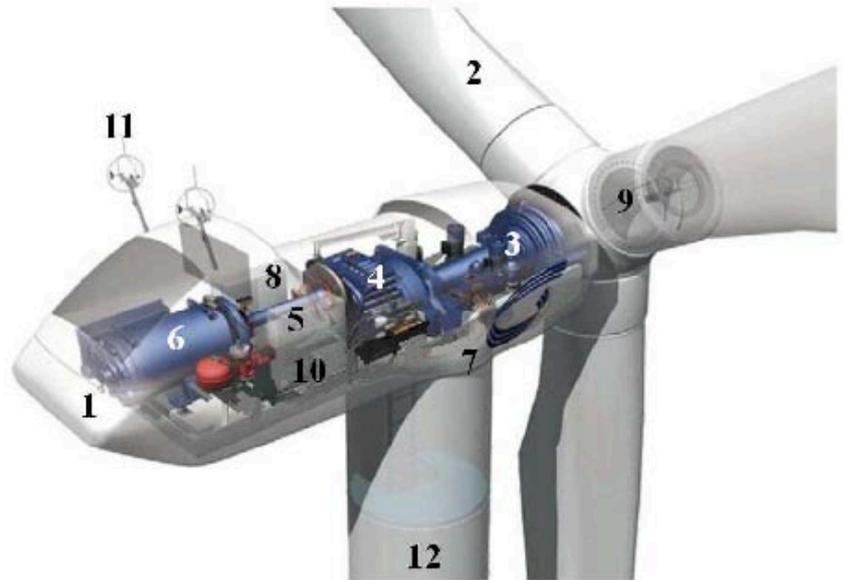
Componenti di una turbina ad asse orizzontale.
